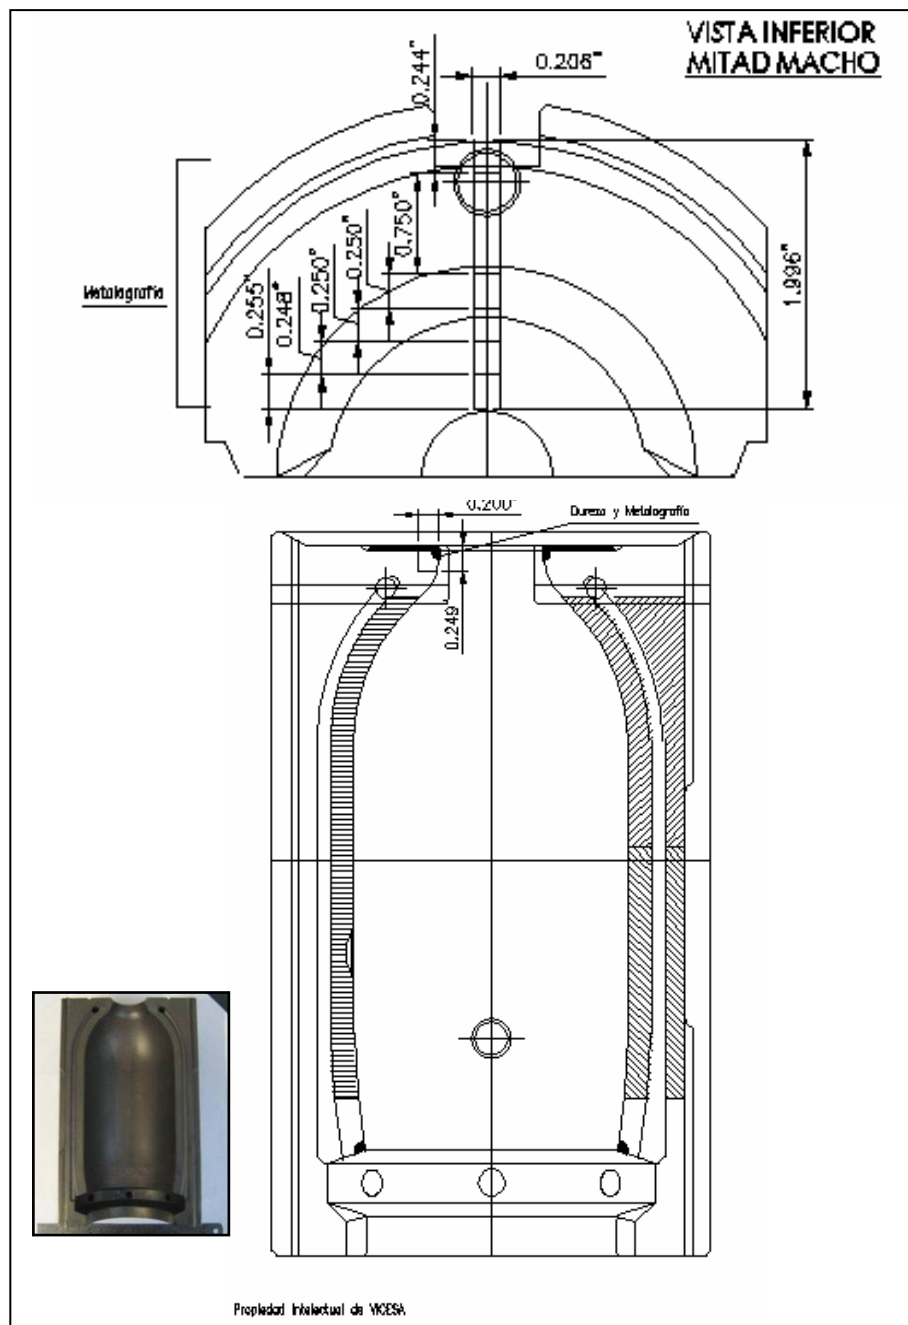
Dibujo del molde de la Moldura C-1615 y en recuadro fotografía de este.
